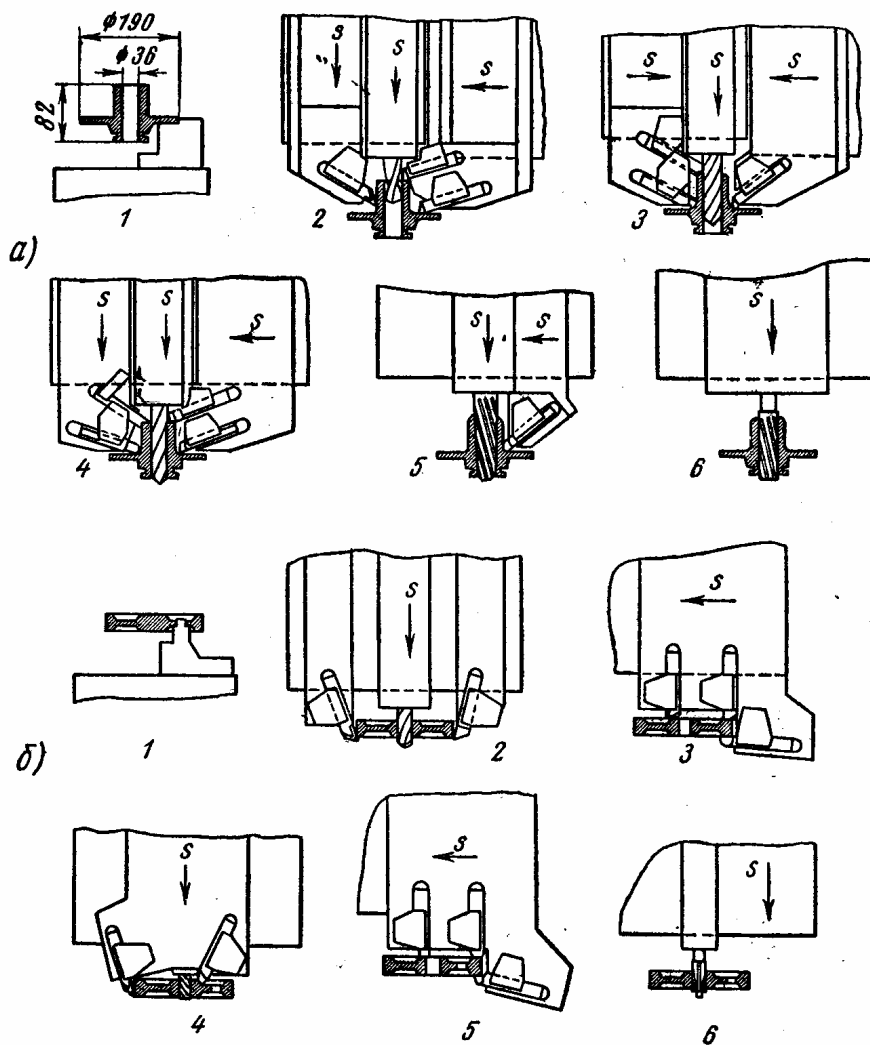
Примеры наладок шестишпindelного вертикального полуавтомата для обработки: *а* – ступицы заднего колеса автомобиля; *б* – зубчатого колеса; 1 – 6 – номера переходов
